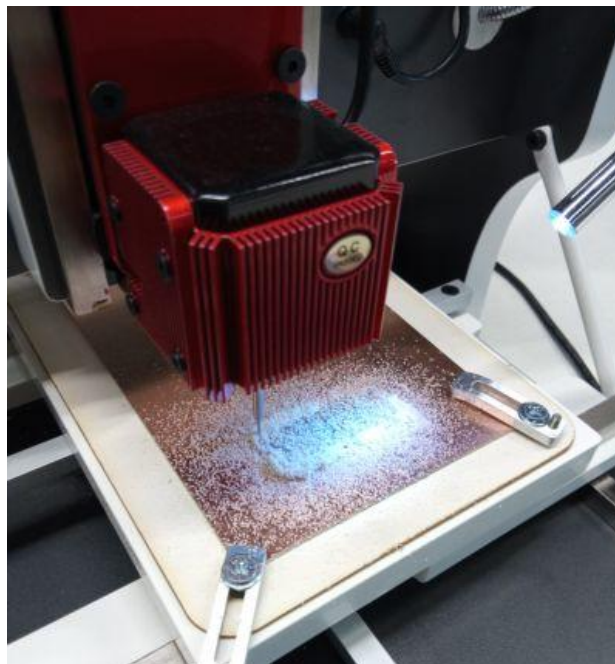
Máquina CNC utilizada para la construcción de la placa PCB
